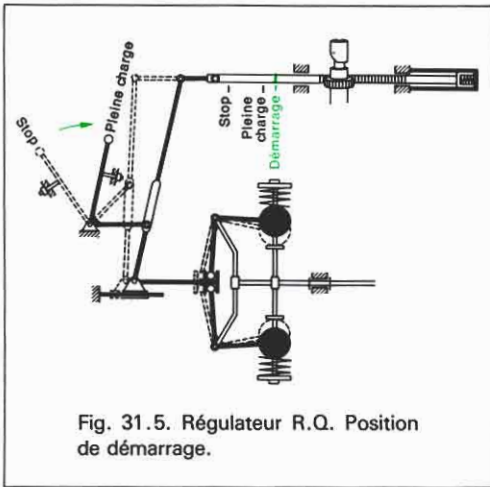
Régulateur R.Q. Position de démarrage.
